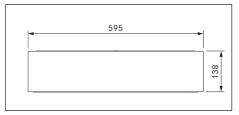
Dimensiones del aparato vista frontal MSS140
